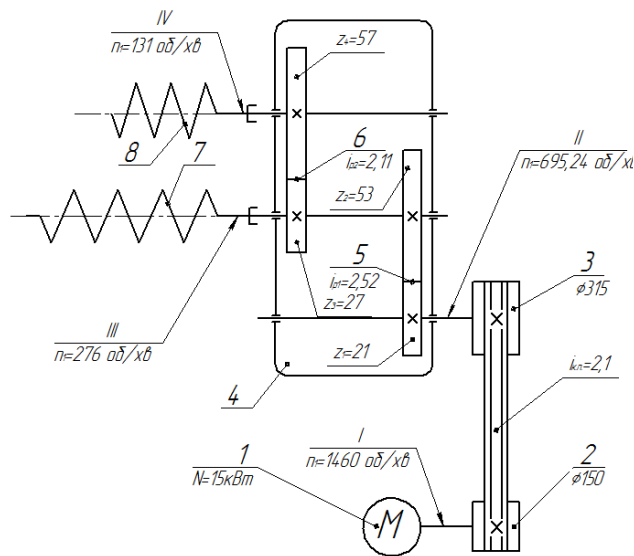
Кінематична схема вовчка МП-2-160: 1 – електродвигун; 2,3 – ведучий і ведений шків клинопасової передачі; 4 – циліндричний редуктор; 5,6 – зубчасті передачі; 7,8 – робочий і допоміжний шнеки.
